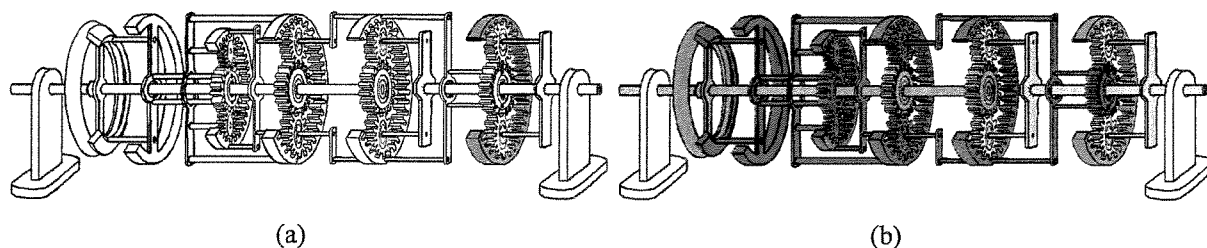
(a) Engrenagem anular do planetário R (destaque); (b) Elementos cujas rotações são as mesmas.
